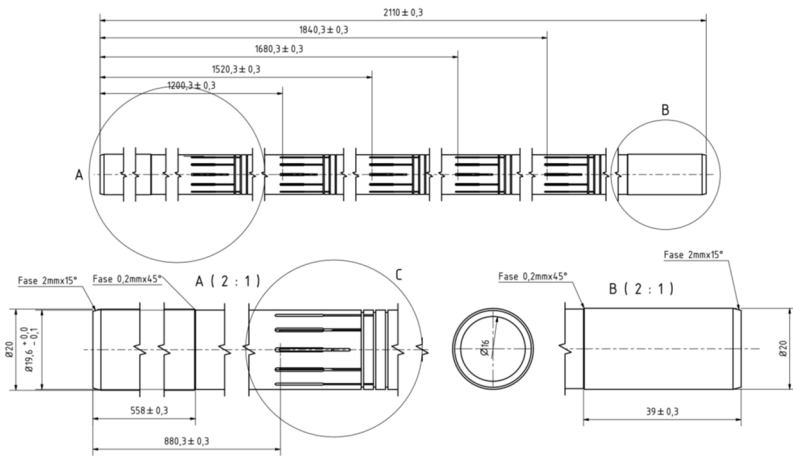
Technische Zeichnung des Messrohres aus Cu-DHP mit Längenangaben und Messebenenpositionen.
